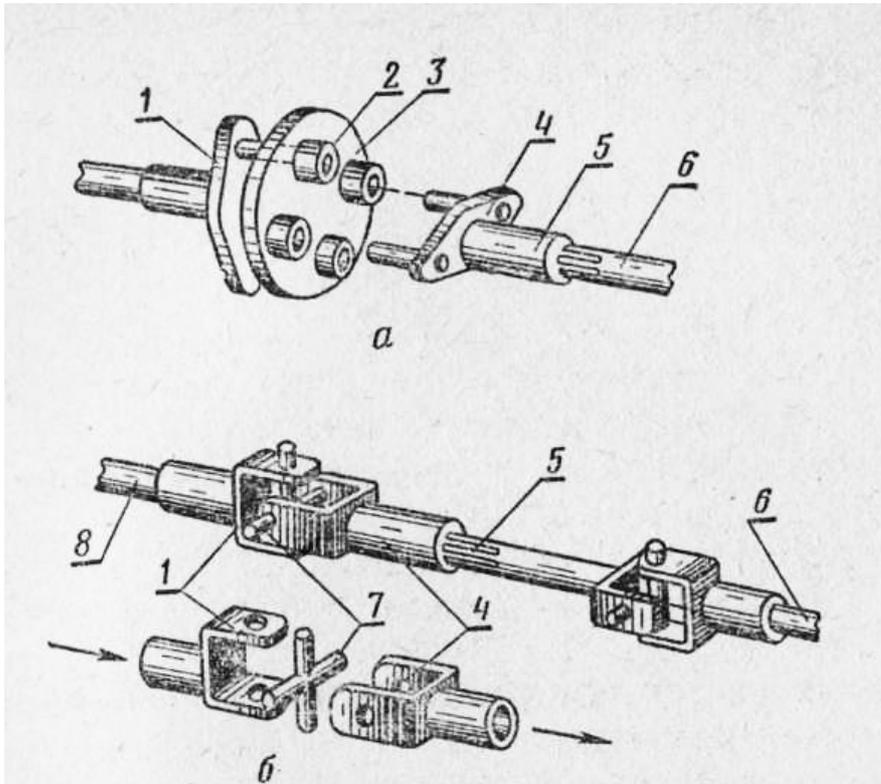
Промежуточное соединение (а) и карданная передача (б): 1 и 4 — ведущая и ведомая вилки; 2 — передаточные элементы; 3 — диск; 5 — шлицевое соединение; 6 — ведомый вал; 7 — крестовина; 8 — ведущий вал
